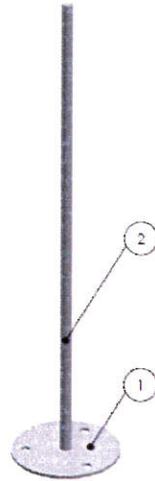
Anschlageinrichtung, Typ: ZS 300-800 III B / B-S / HD-B
